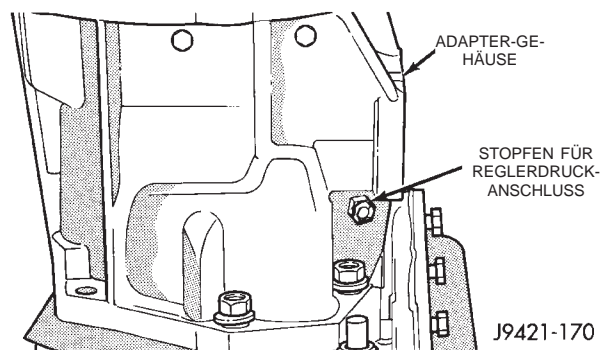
Prüfanschlüsse auf der Gehäuse-Rückseite—Heckantrieb
